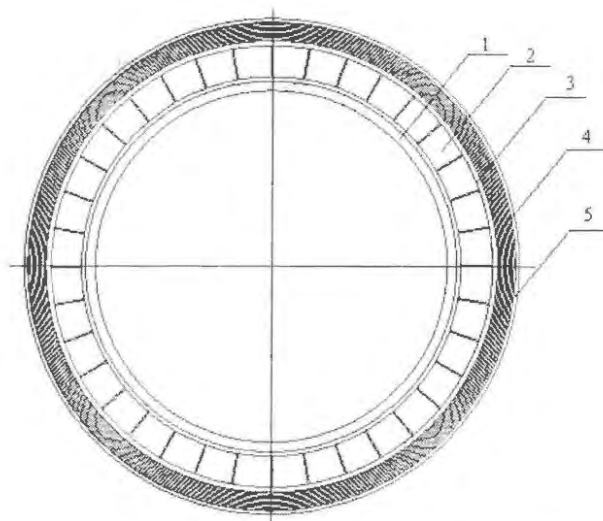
Поперечное сечение реактора с намоткой струны с внутренним давлением 200 атм: 1 – оболочка корпуса; 2 – ОК с ребрами с промежуточным давлением; 3 – кольцо оболочки, на которую наматывается струна; 4 – намотка струны; 5 – внешний кожух
